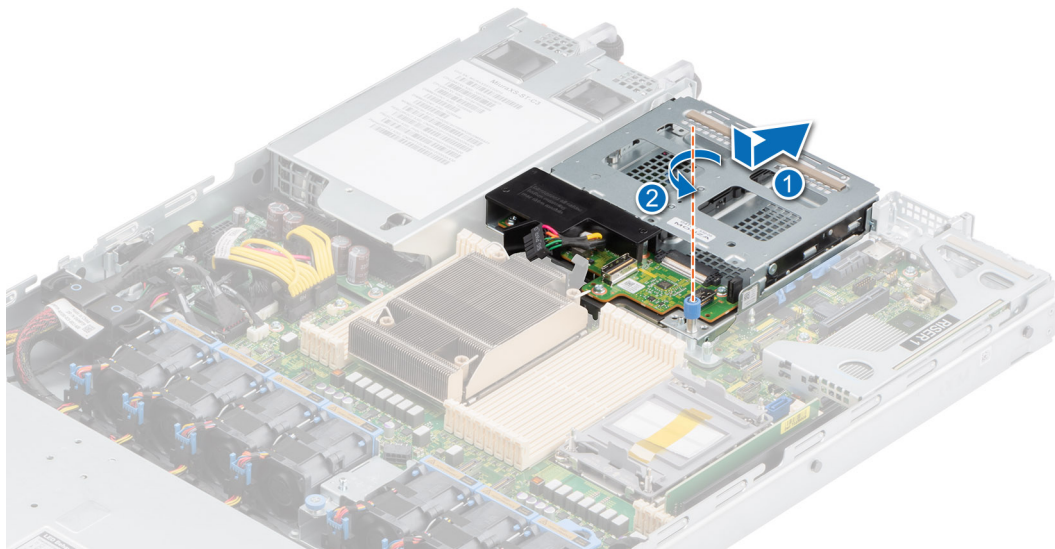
Einbauen des hinteren 2,5-Zoll-Laufwerksgehäuses
